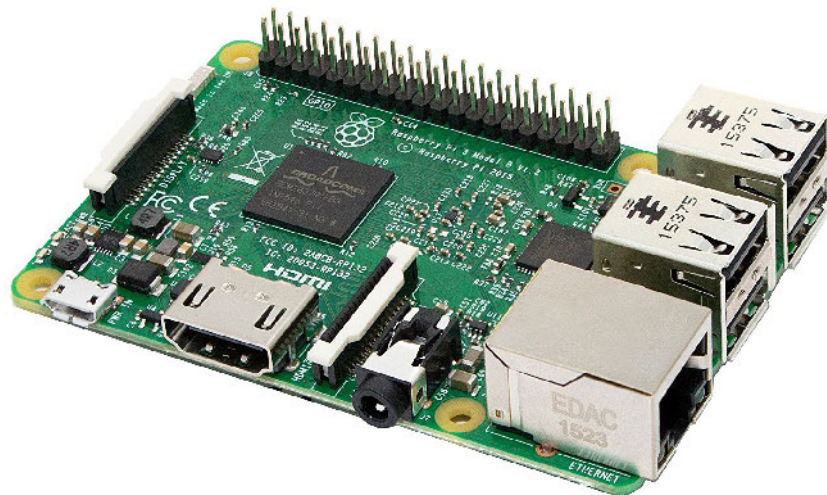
La photographie d'un PCB avec des composants assemblés [1].
